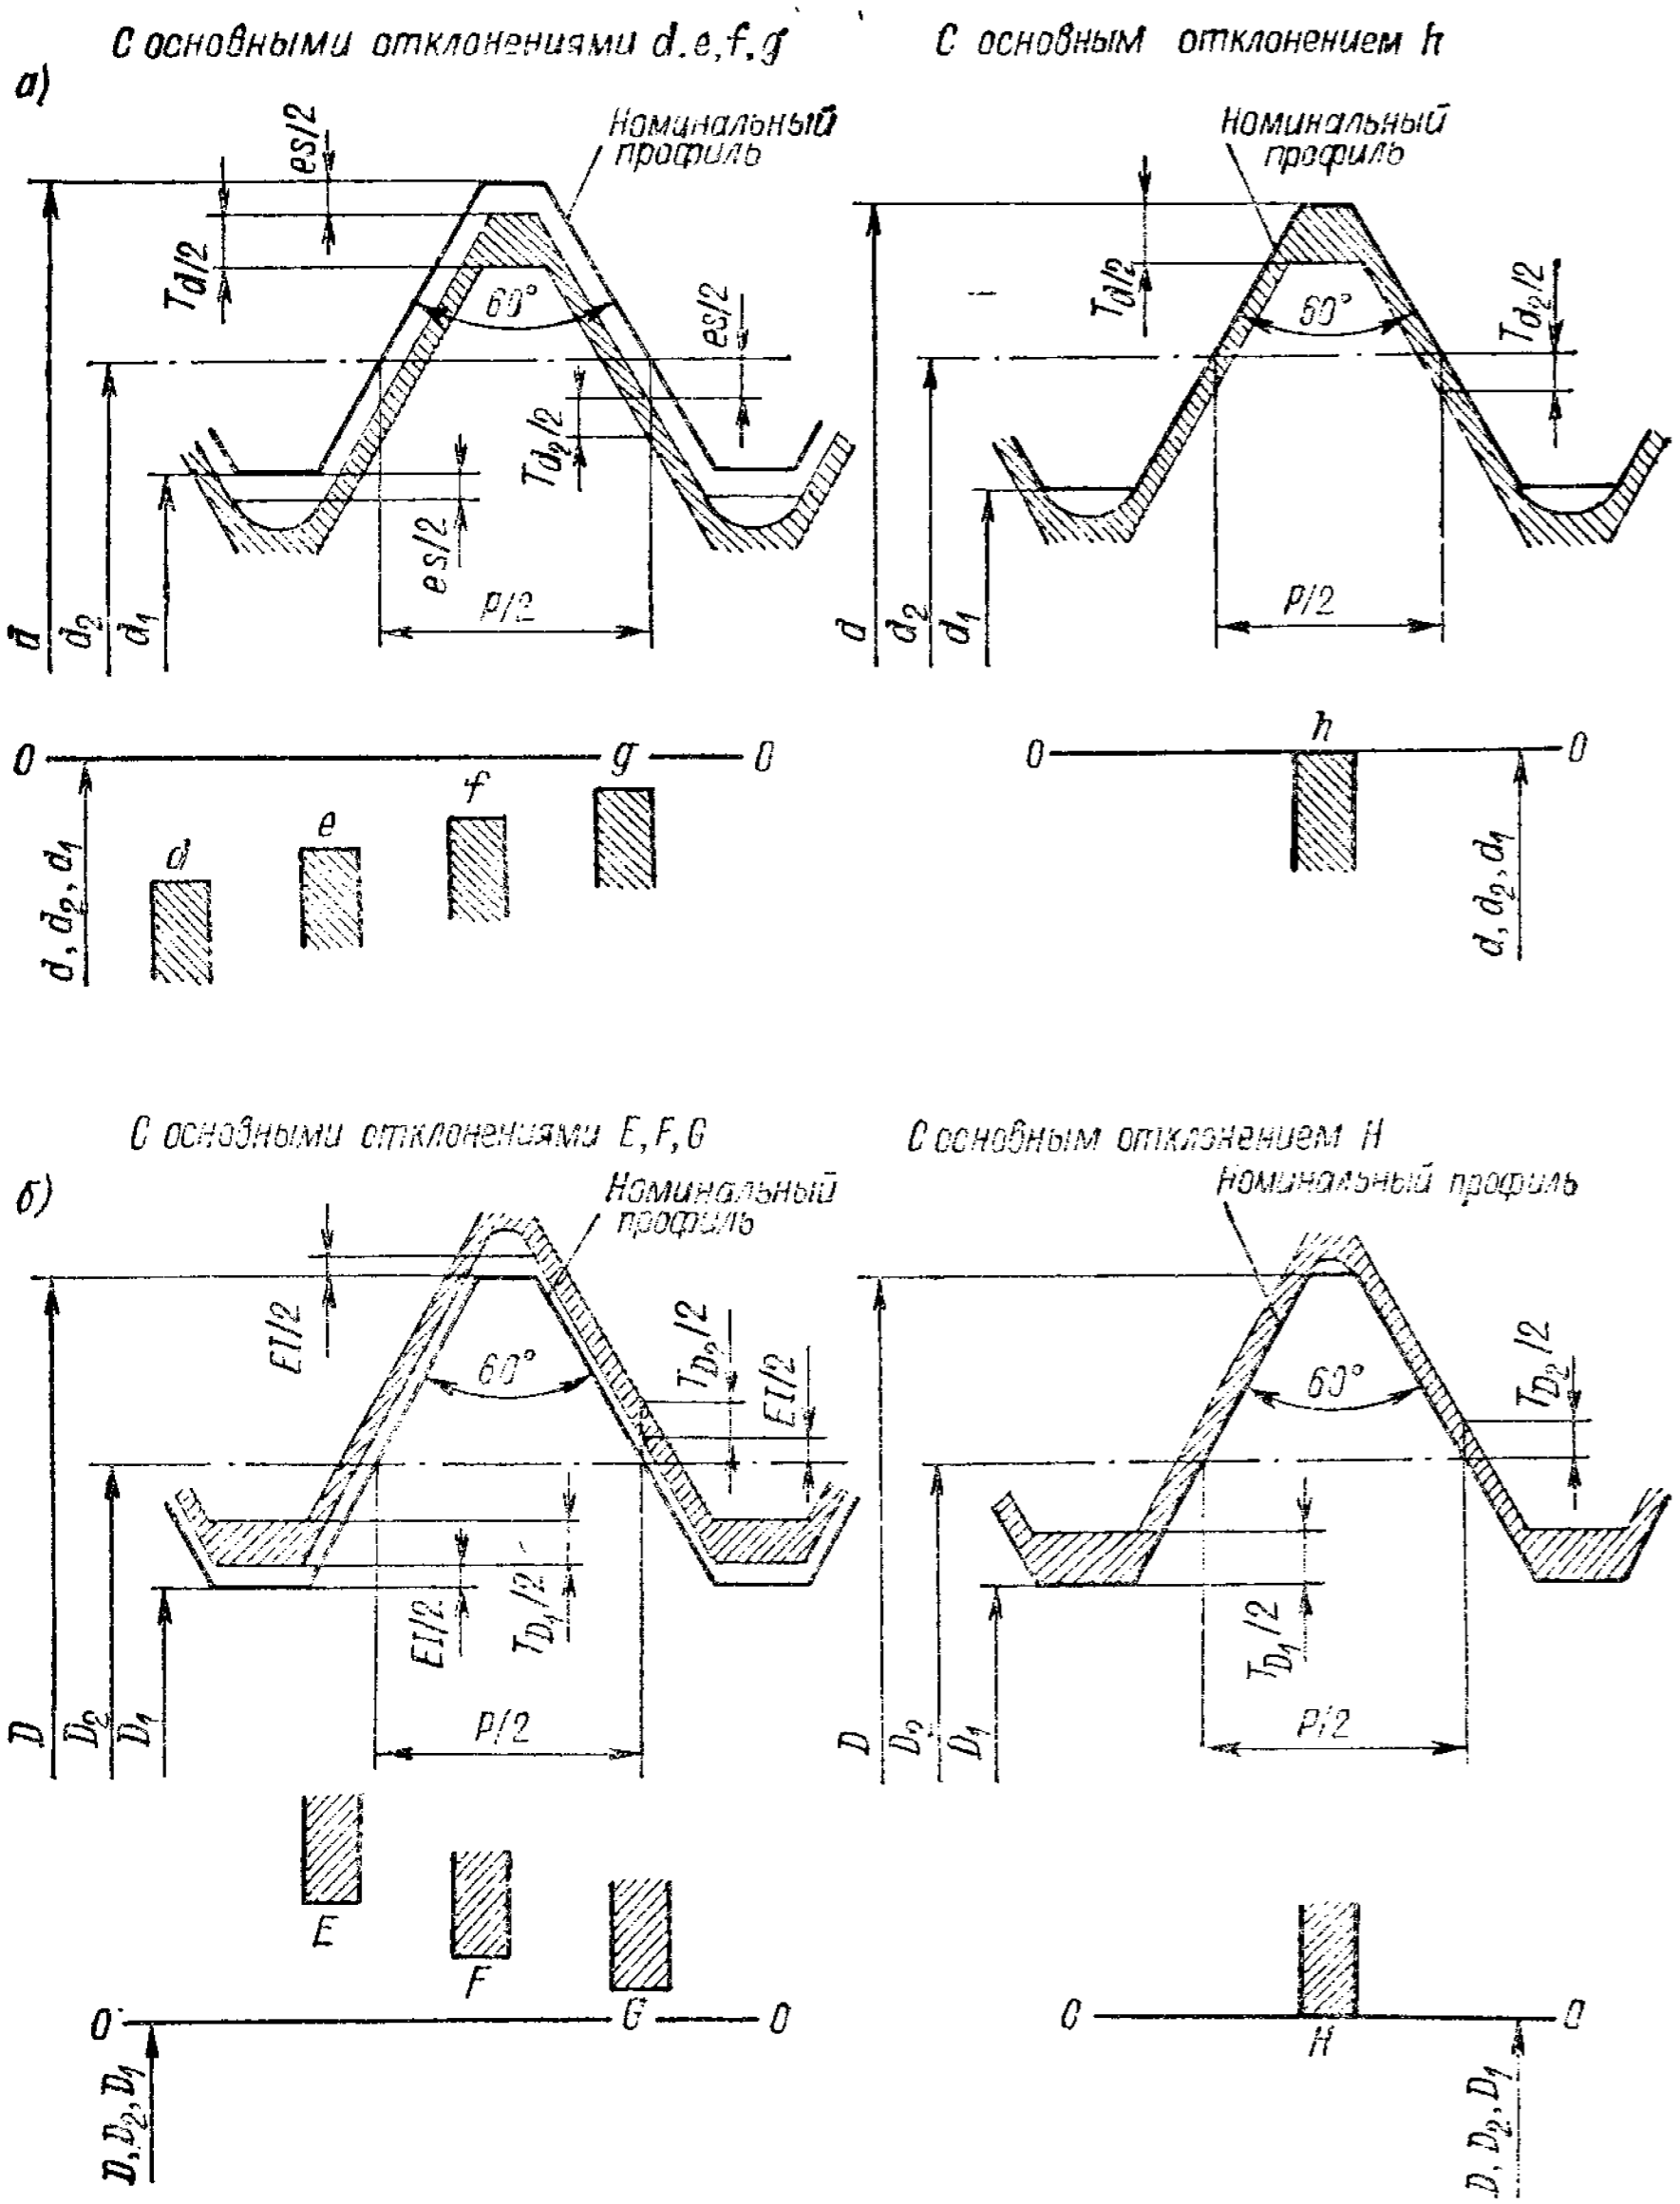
Расположение полей допусков наружной (а) и внутренней (б) метрической резьбы в посадках с зазором
